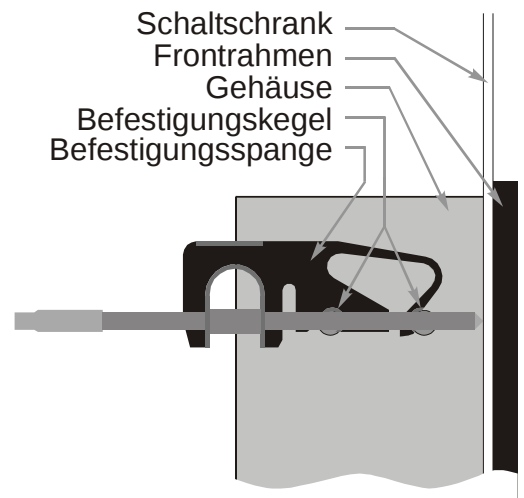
Seitenansicht - mit Befestigungsklammer
